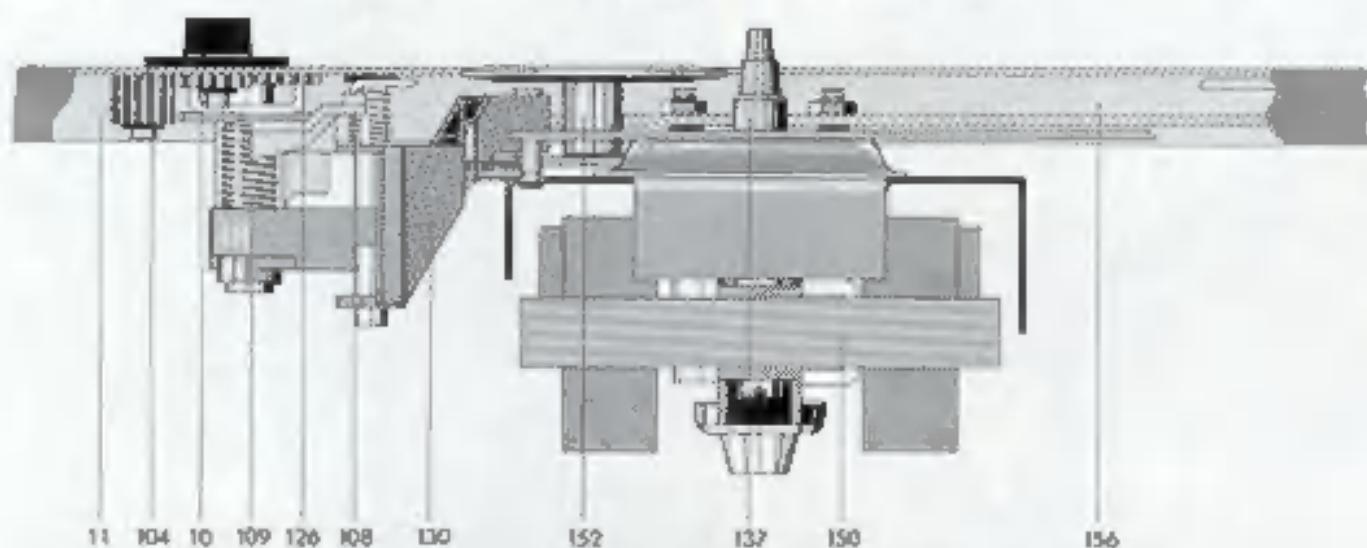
Motoraufhängung und Antrieb des Plattentellers Dual 1222
